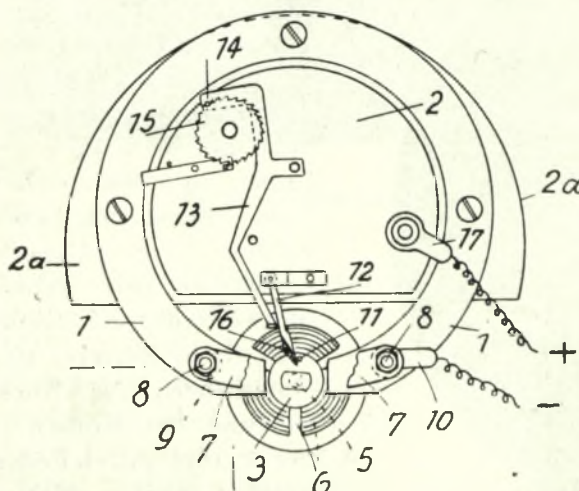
Henker-Neuelektro-Uhr, Rückansicht
